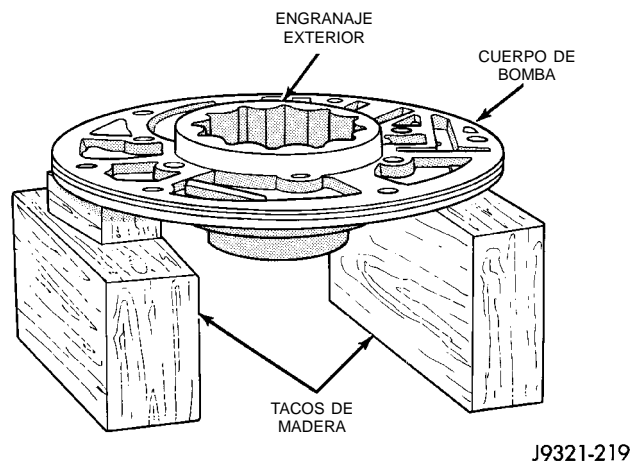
Apoyo de la bomba e instalación del engranaje exterior
